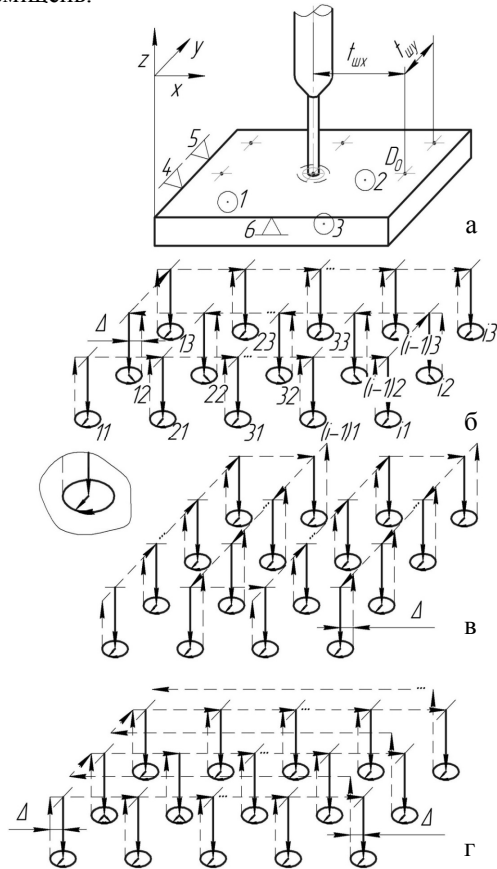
Встановлення заготовки на робочому столі верстата (а) та послідовність виконання масивуотворів на оброблюваній заготовці: (б, в) – змійкових обхід; г) обхід із
